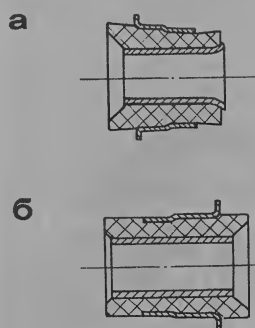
Резино-металлические шарниры рычагов подвески (а — верхнего, б — нижнего).
